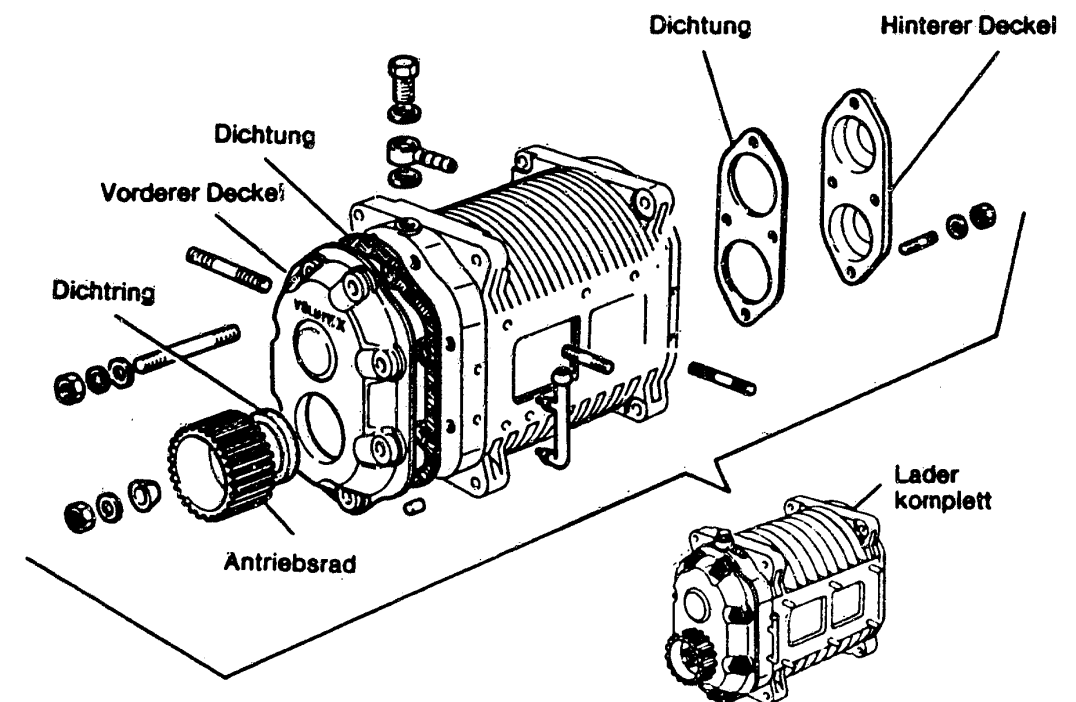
Die bezeichneten Einzelteile am Roots-Kompressor sind als Ersatzteile erhältlich.
